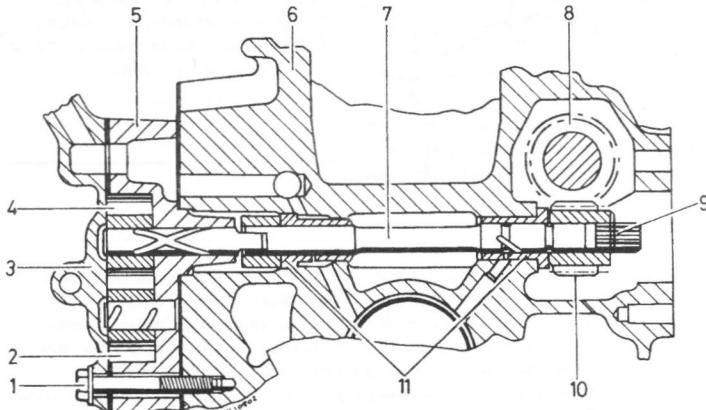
Вид в разрезе масляного насоса и конструкции приводного вала (Раздел 32)
